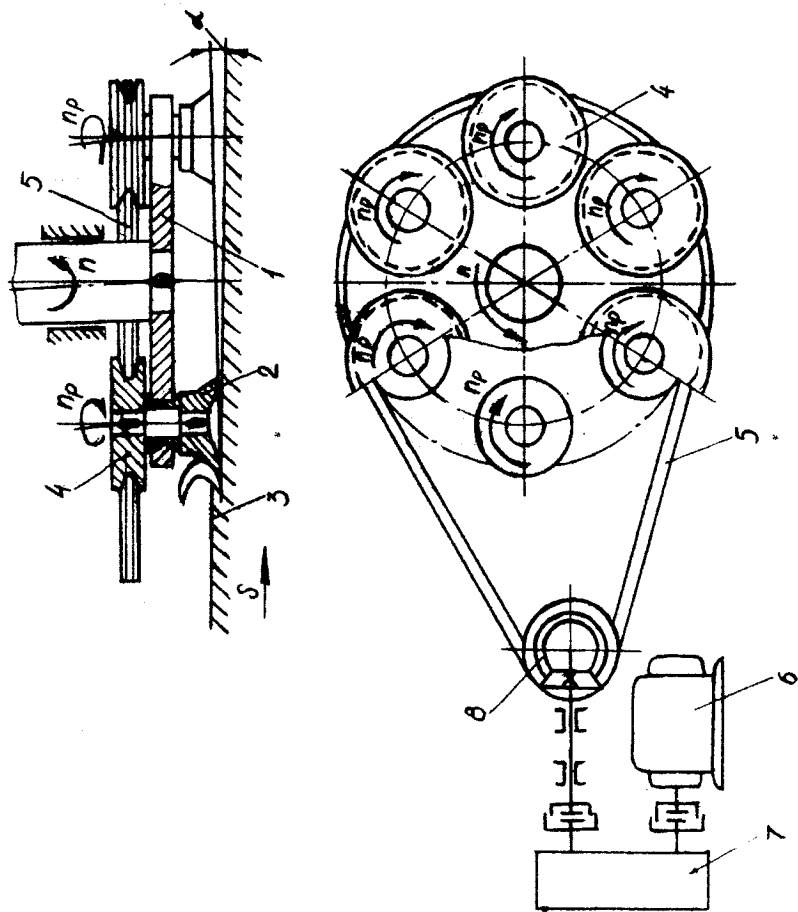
Планетарна головка для ротaційного фрезерування
